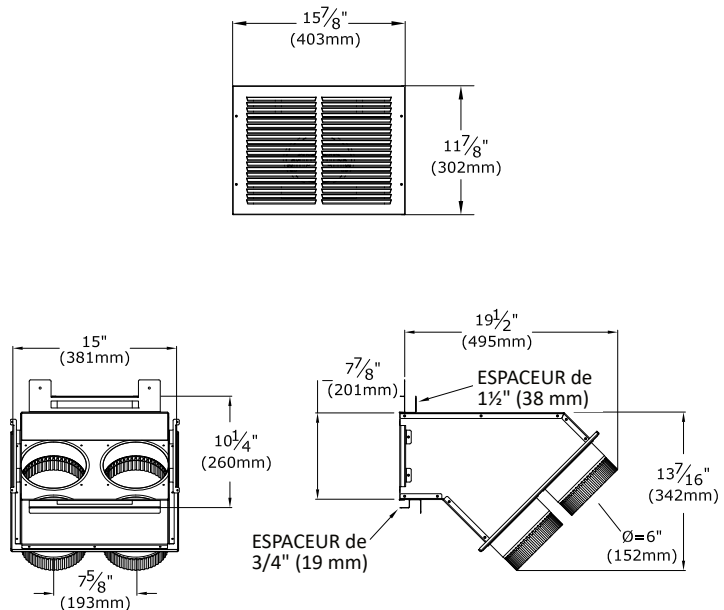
Vue d'ensemble du kit KZK-1510B
